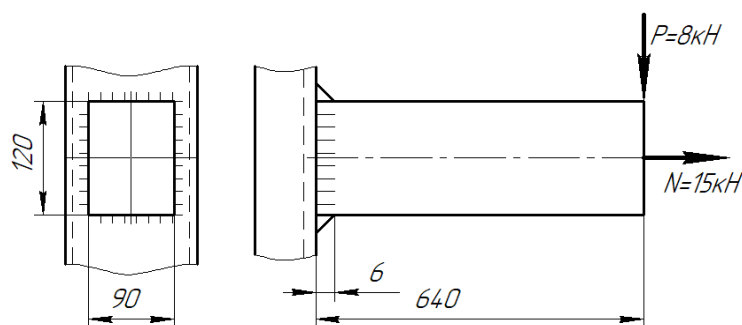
Сварное соединение бруска со швеллером
